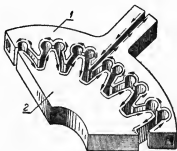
Схема индукционного нагрева цилиндрической шестерни:
